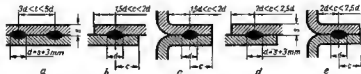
Dimensiones de las costuras por puntos y por contacto de rodillo.
